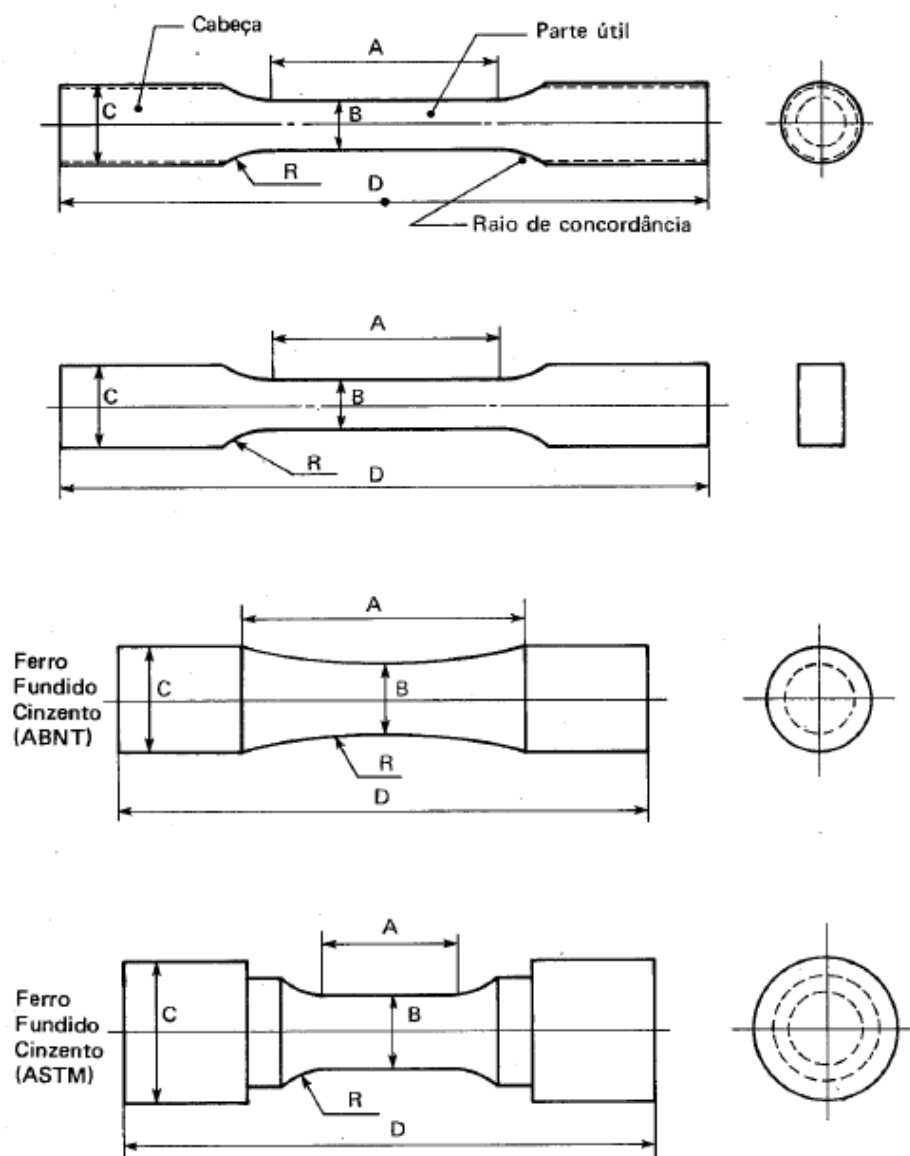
Corpos de prova para ensaio de tração (SOUZA, 1982).
